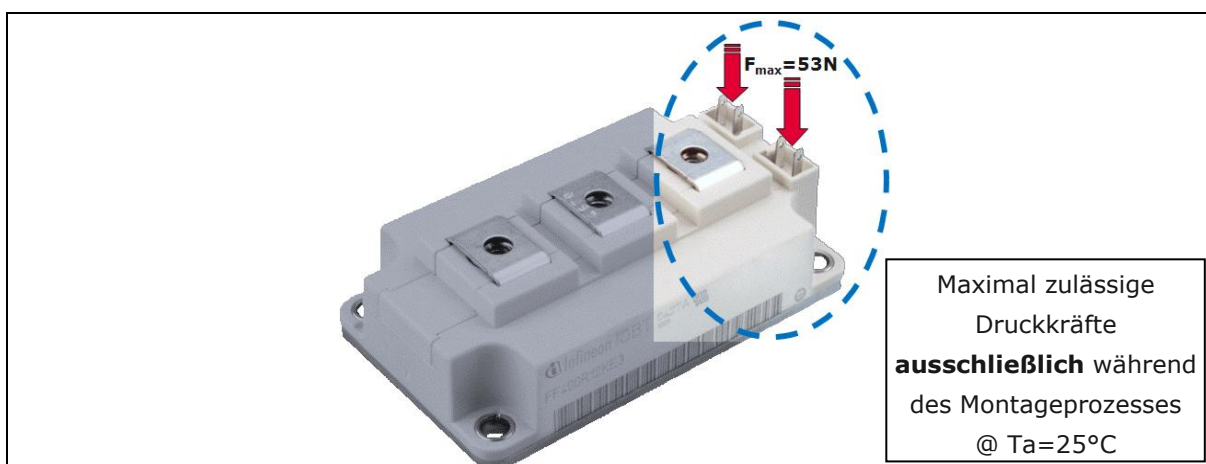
Maximal zulässige Druckkraft auf die Steuerkontakte der 62mm halbbrücken Gehäuse variante
